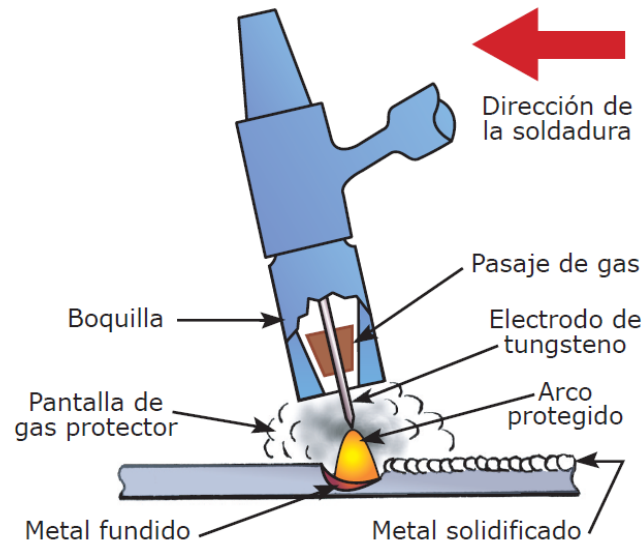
Esquema de un soplete para soldadura TIG
